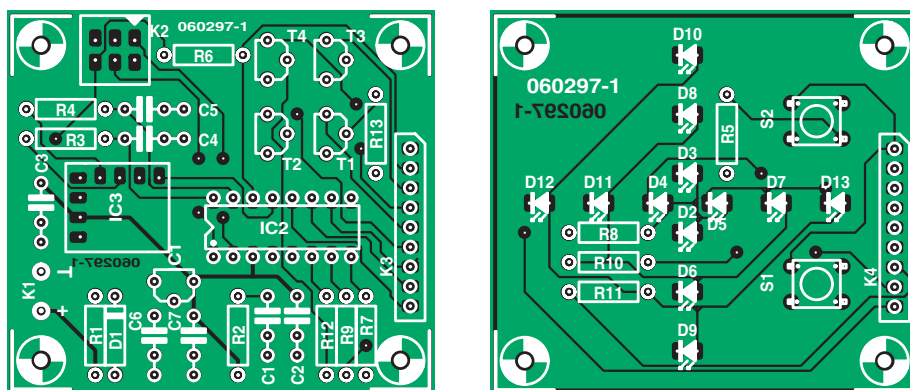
Tracé des pistes et disposition des composants des deux platines à meubler avant leur assemblage à impériale.
